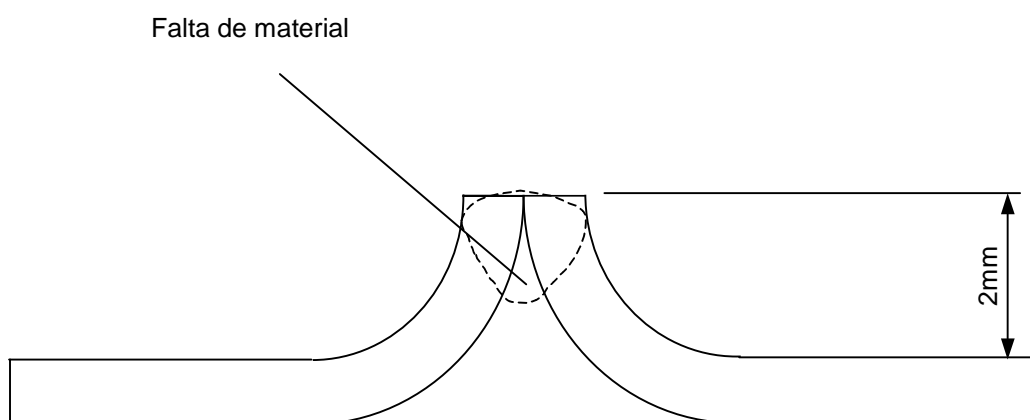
Falta de material na poça de fusão (flange 2mm).
